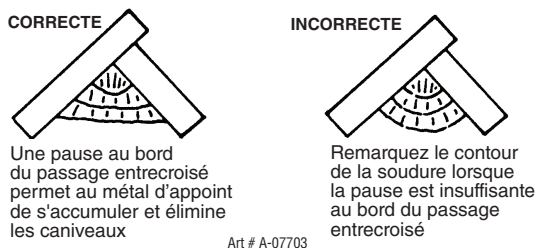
Exemples de soudure d'angle verticale
